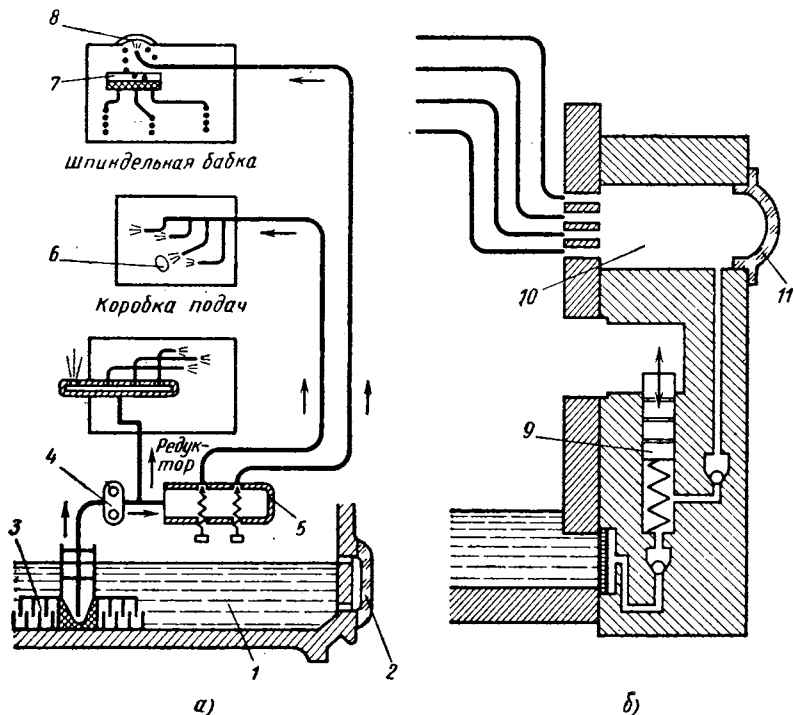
Схема смазки станков 1Н318 и 1Н318Р:
